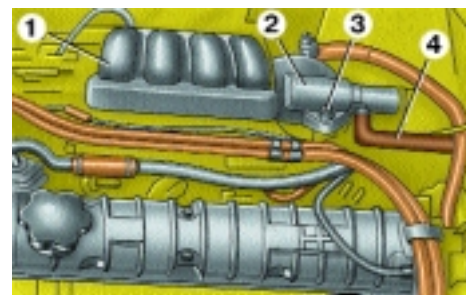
Расположение регулятора холостого хода на двигателе F3R 272: 1 – воздушный ресивер двигателя; 2 – регулятор холостого хода; 3 – болт крепления регулятора; 4 – шланг подвода дополнительного воздуха
